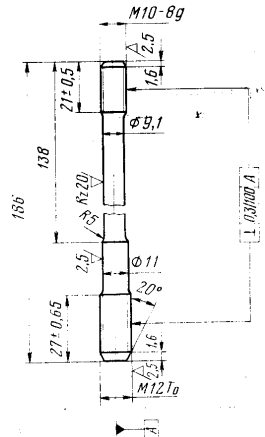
Шпилька крепления головок цилиндров (ремонтная) Сталь 40Х. Твердость HRC 23... 29
